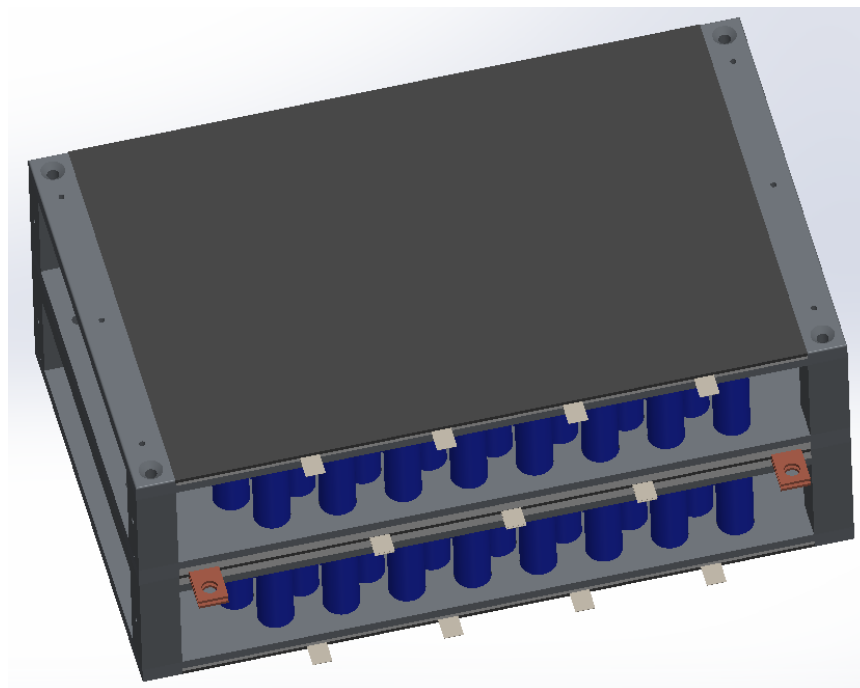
Общий вид аккумуляторной сборки без корпуса
